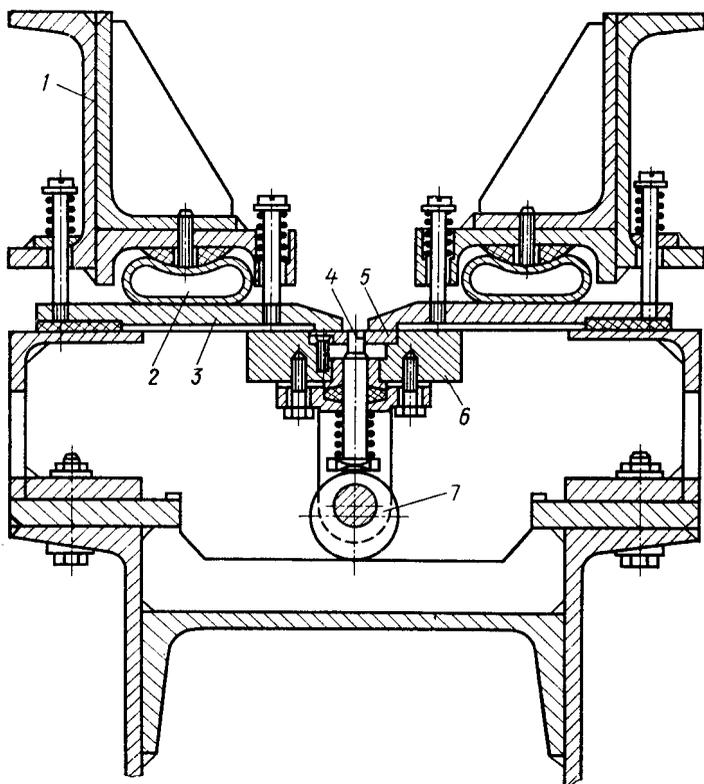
Приспособление для сборки и сварки прямолинейных стыков тонколистовых элементов
